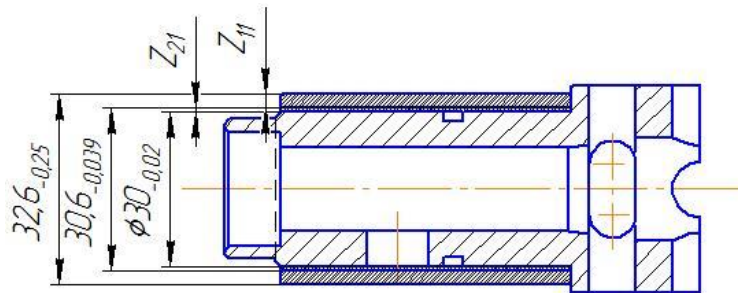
Эскиз диаметального припуска для поверхности 4
